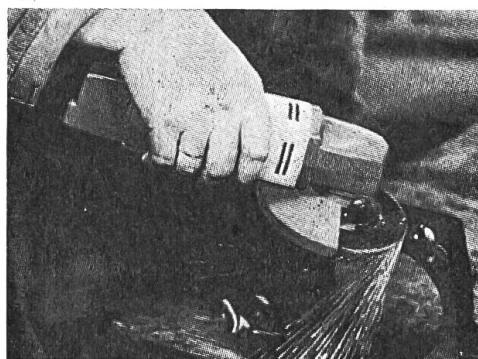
Il ne faut considérer la meuleuse angulaire à main que comme une machine auxiliaire car elle se trouverait constamment soumise à des contraintes excessives en tant que machine unique.
